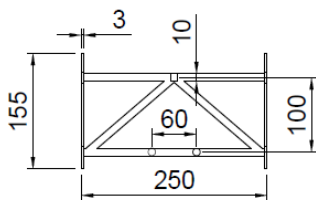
Vista frontal do elemento anelar estrutural e tirantes (medidas em milímetros).
